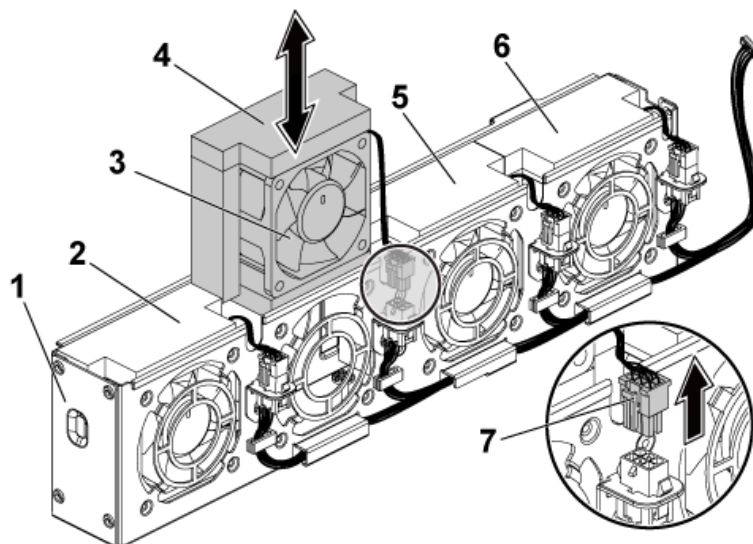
Retrait et installation d'un ventilateur de refroidissement
